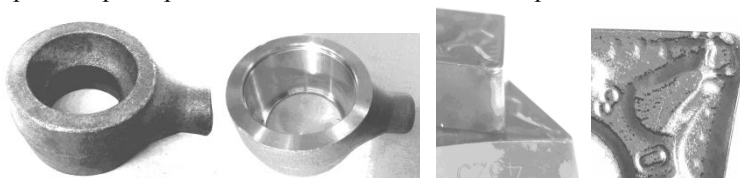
Заготовка, деталь и нормальный износ пластины
